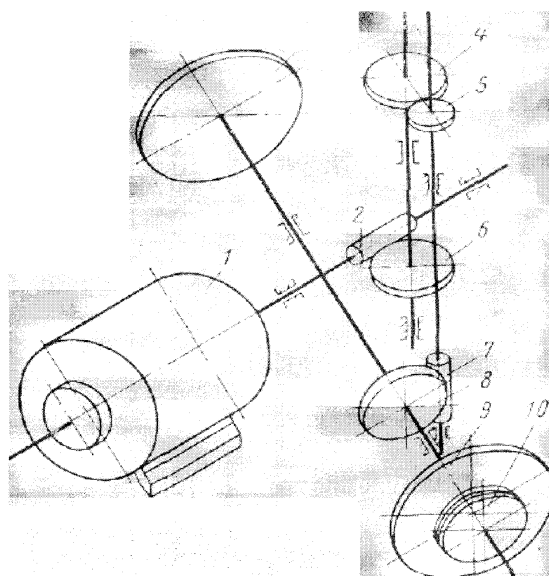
Кинематическая схема ведущего механизма газорезательной машины «Радуга»
